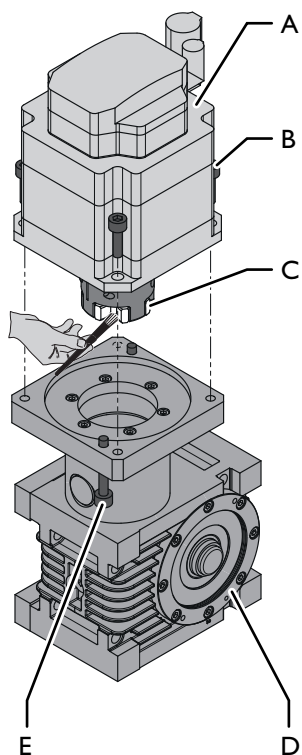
Смонтировать мотор: Блок редуктора Güdel
